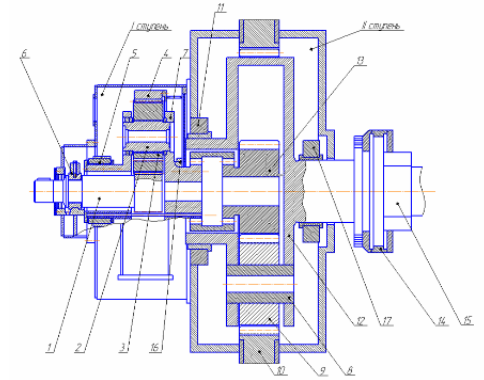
Планетарный редуктор существующей конструкции: 1 - вал-шестерня I ступени; 2, 8 - ось сателлита; 3, 9 - сателлит; 4, 10 - зубчатый венец; 5, 11, 16, 17 - подшипники скольжения водила; 6 - подшипники скольжения вала-шестерни I ступени; 7, 12 - водило; 13 - солнечная шестерня II ступени; 14 - зубчатая муфта; 15 - промвал
